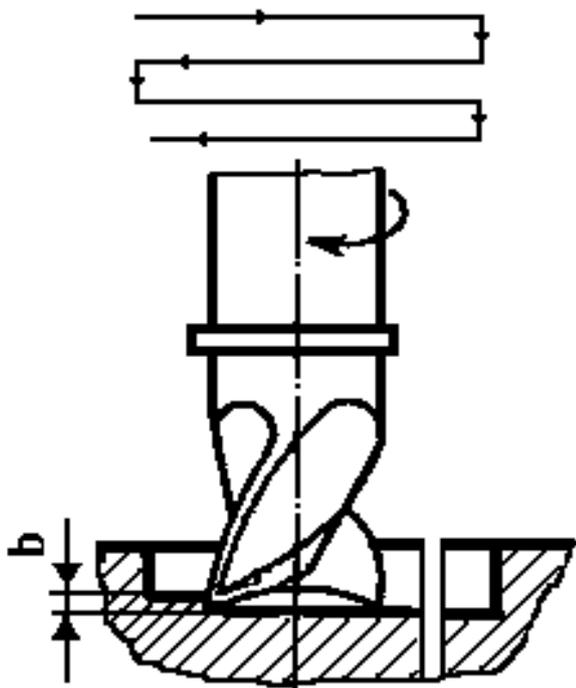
Схема фрезерования 2-х зубой фрезой.
